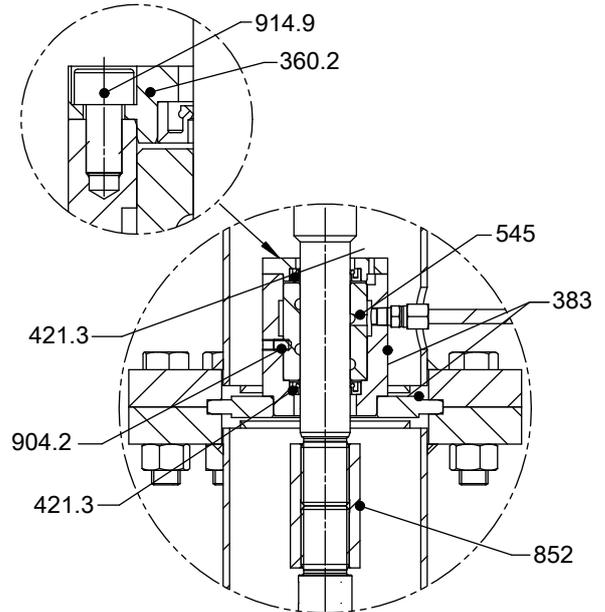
Detailzeichnungen Gewindekupplung (nur bei Ausführung mit 2 oder 3 Zwischenrohren)
